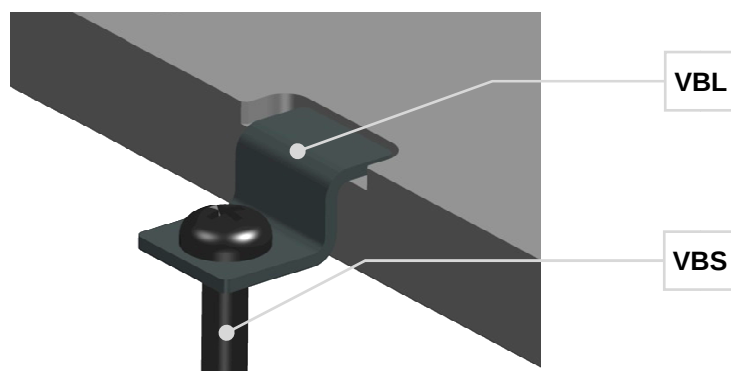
Присоединение прибора винтами с помощью пластин крепления
